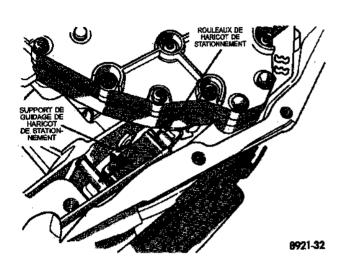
Pousser les rouleaux de tige de stationnement depuis le support de guidage
